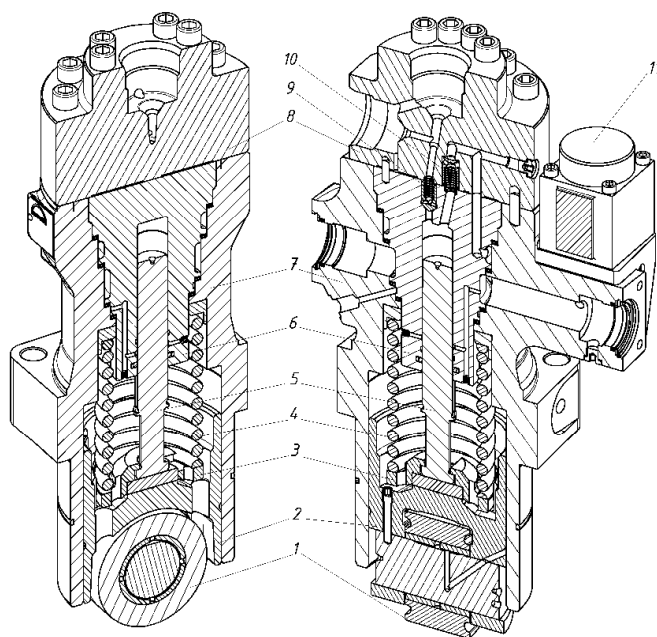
Паливний насос високого тиску двигунів типу 32/44CR фірми MAN. 1 – ролик штовхача; 2 – штовхач; 3 – нижня тарілка поворотної пружини; 4 – поворотна пружина; 5 – плунжер; 6 – втулка плунжера; 7 – корпус; 8 – кришка; 9 – нагнітальний клапан; 10 – наповнювальний клапан; 11 – дросельний клапан керування подачею з електромагнітним приводом
